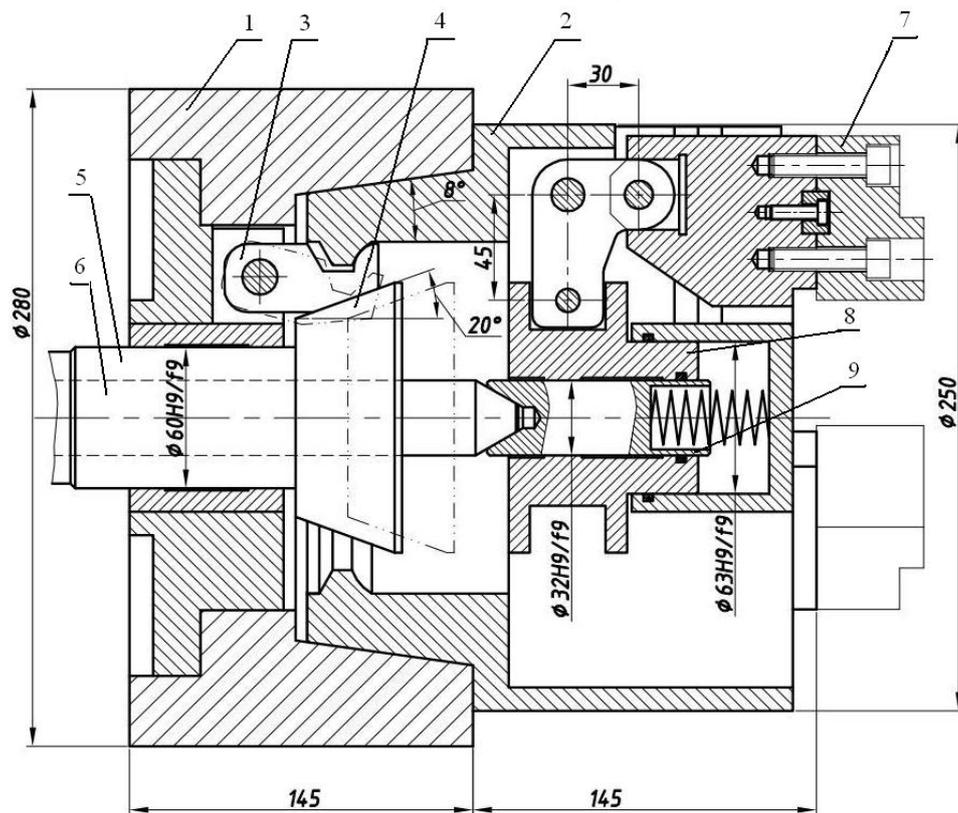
Патрон токарный с механическим устройством для закрепления наладок и гидропластмассовым устройством для закрепления заготовок
